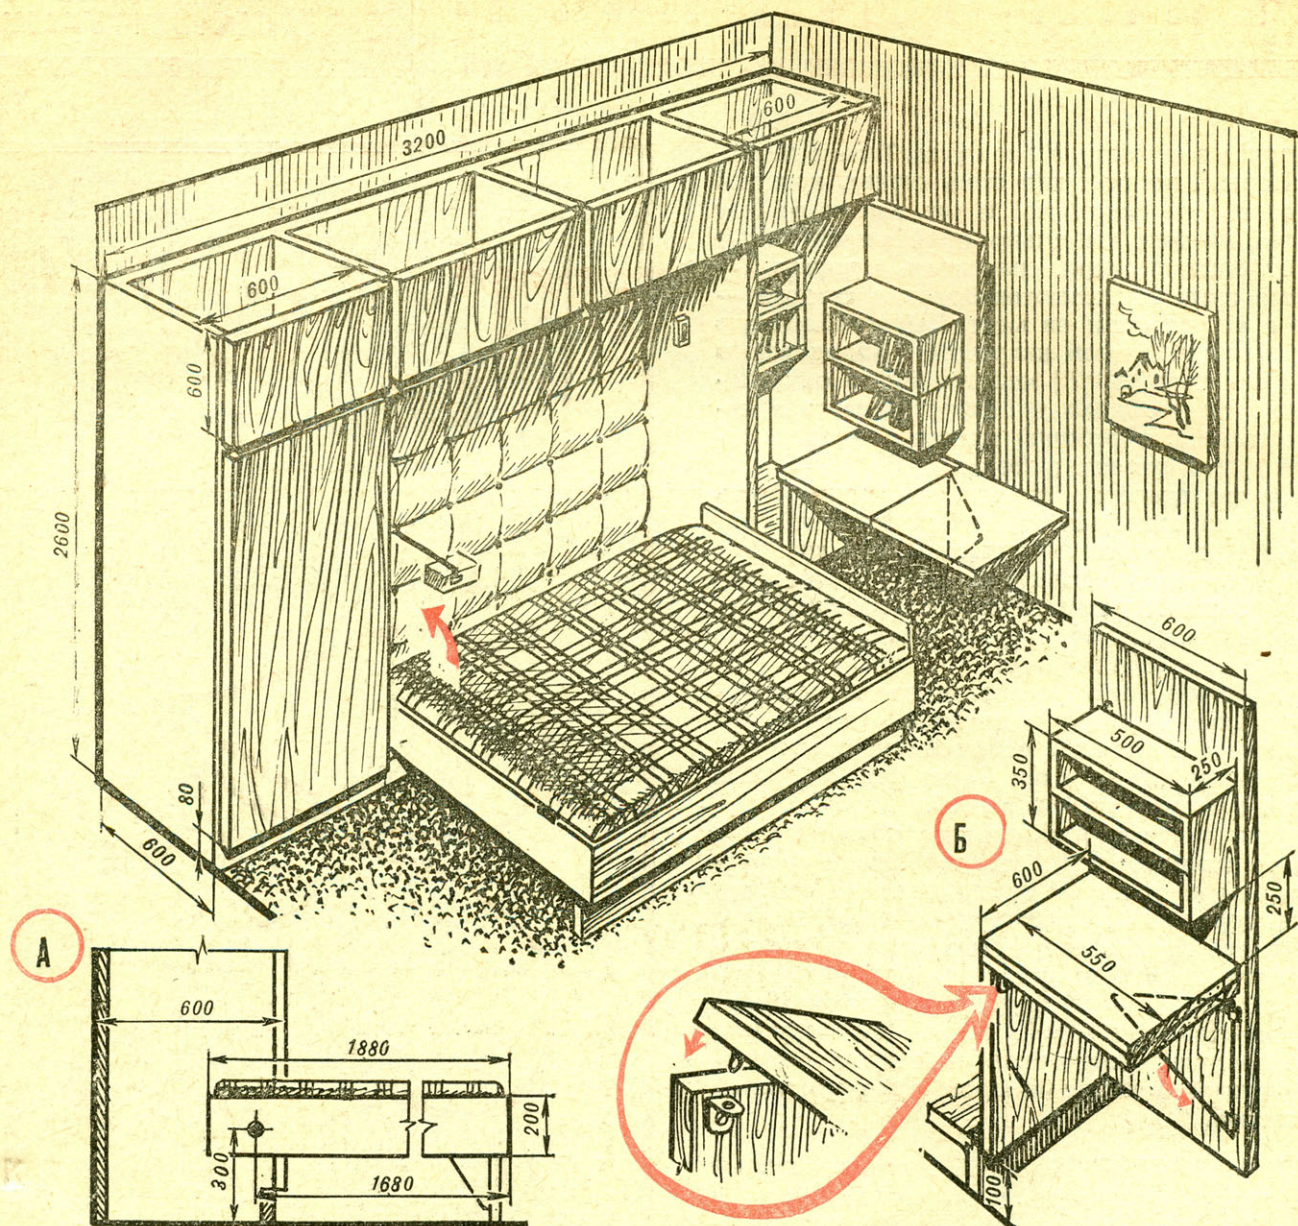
Вариант решения кроватиной секции — с продольной двухспальной лежанкой: А — схема узла кровати в опущенном состоянии, Б — вариант рабочего уголка.
